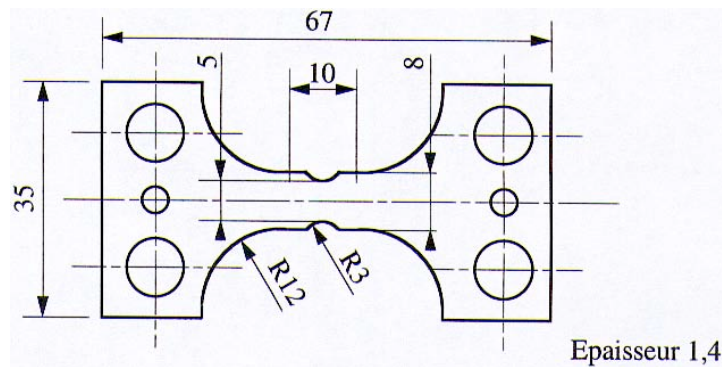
éprouvettes de fatigue sur GLARE 2
